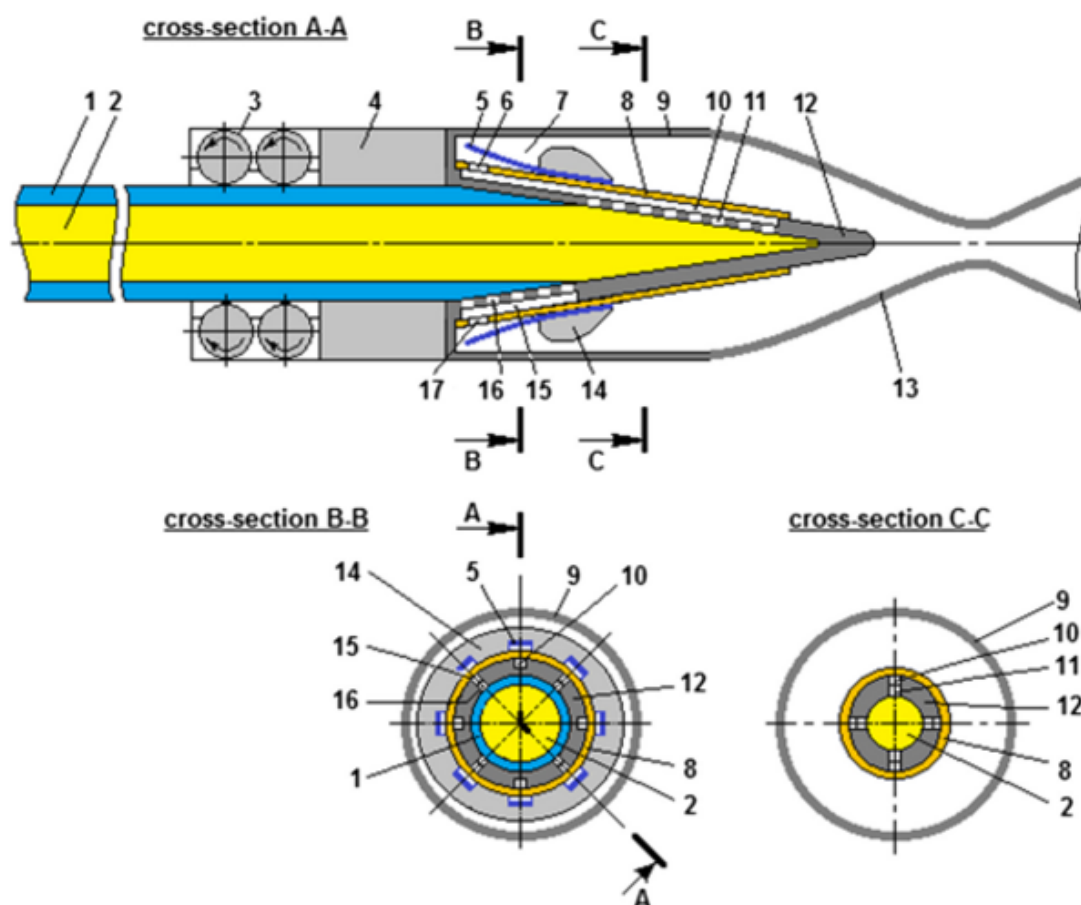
1 – тверде полімерне пальне; 2 – твердий окислювач; 3 – електромеханічні колеса подачі; 4 – обтюратор; 5 – зворотні клапани; 6 – форсунки окислювача; 7 – змішувальна камера; 8 – кришка; 9 – камера згоряння; 10 – канали збору окислювача; 11 – отвори збору окислювача; 12 –
